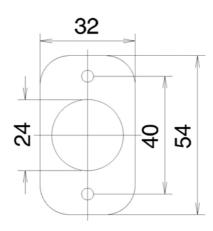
Габаритные и присоединительные размеры реле потока воздуха и монтажного хомута
